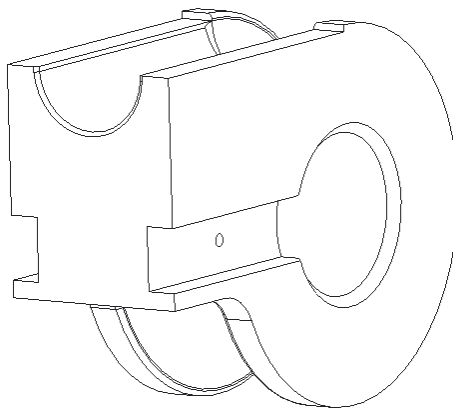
bending tool disegnato con il software PTC Creo.
